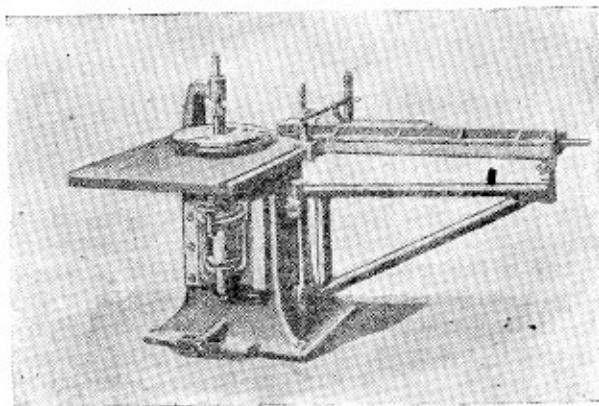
Фрезерный станок с прорезным диском и кареткой
